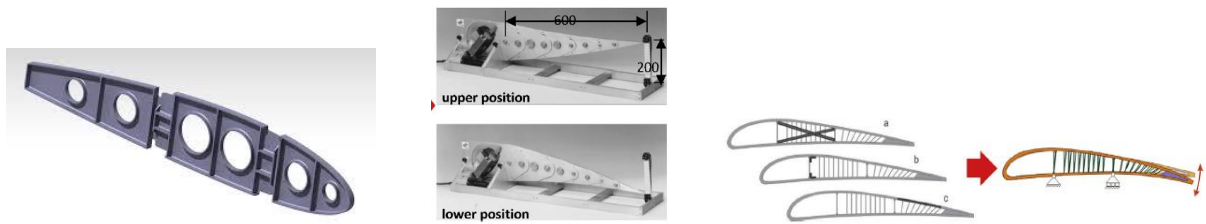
Photo d'un rib rigide d'aile d'avion [7] (à gauche). Photo d'un rib avec des plaques articulées [5](au milieu). Photo d'un belt-rib [6](à droite)
